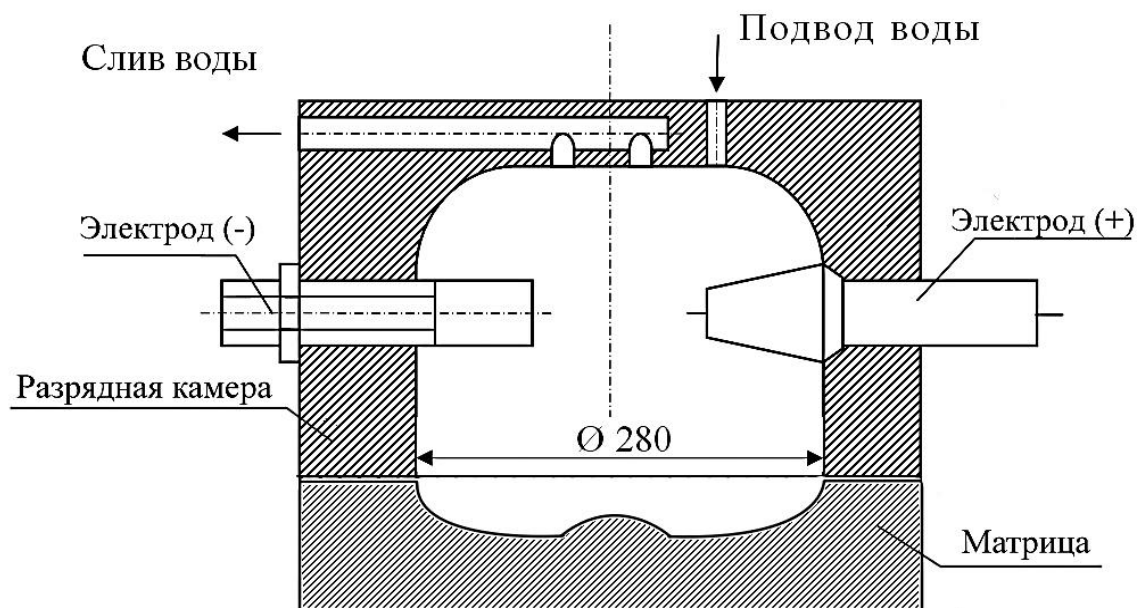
Разрядная камера и матрица для ЭГ штамповки листовых деталей
